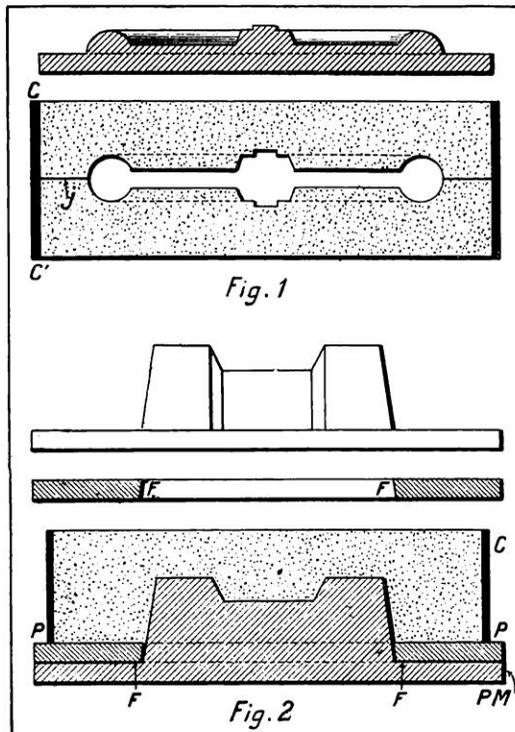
MOULAGE D'UN VOLANT DE MACHINE DONT LES DEUX FACES SONT SEMBLABLES
